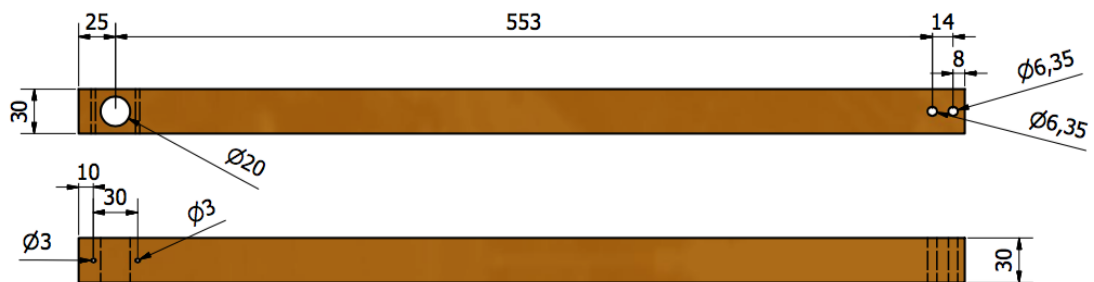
DIMENSIONES EJE CONECTOR
